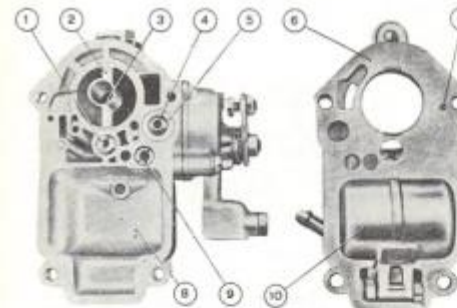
WEBER karburator type 26 IMB 1 med aftaget svømmerhusdæksel.
